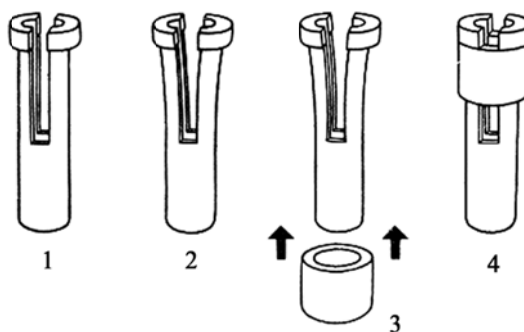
Метод сборки соединителя из МПФ: 1 – изготовление щели; 2 – разгибание торцевой части; 3 – надевание кольца из сплава с эффектом запоминания формы; 4 – деталь в собранном виде [13, стр. 168].
